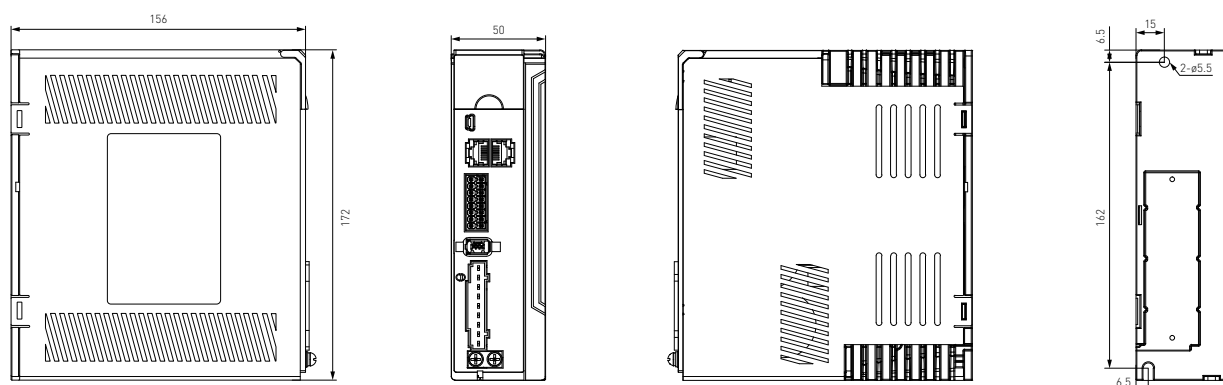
Габаритные размеры драйверов EL7-EC750F/1000F (размер B).
